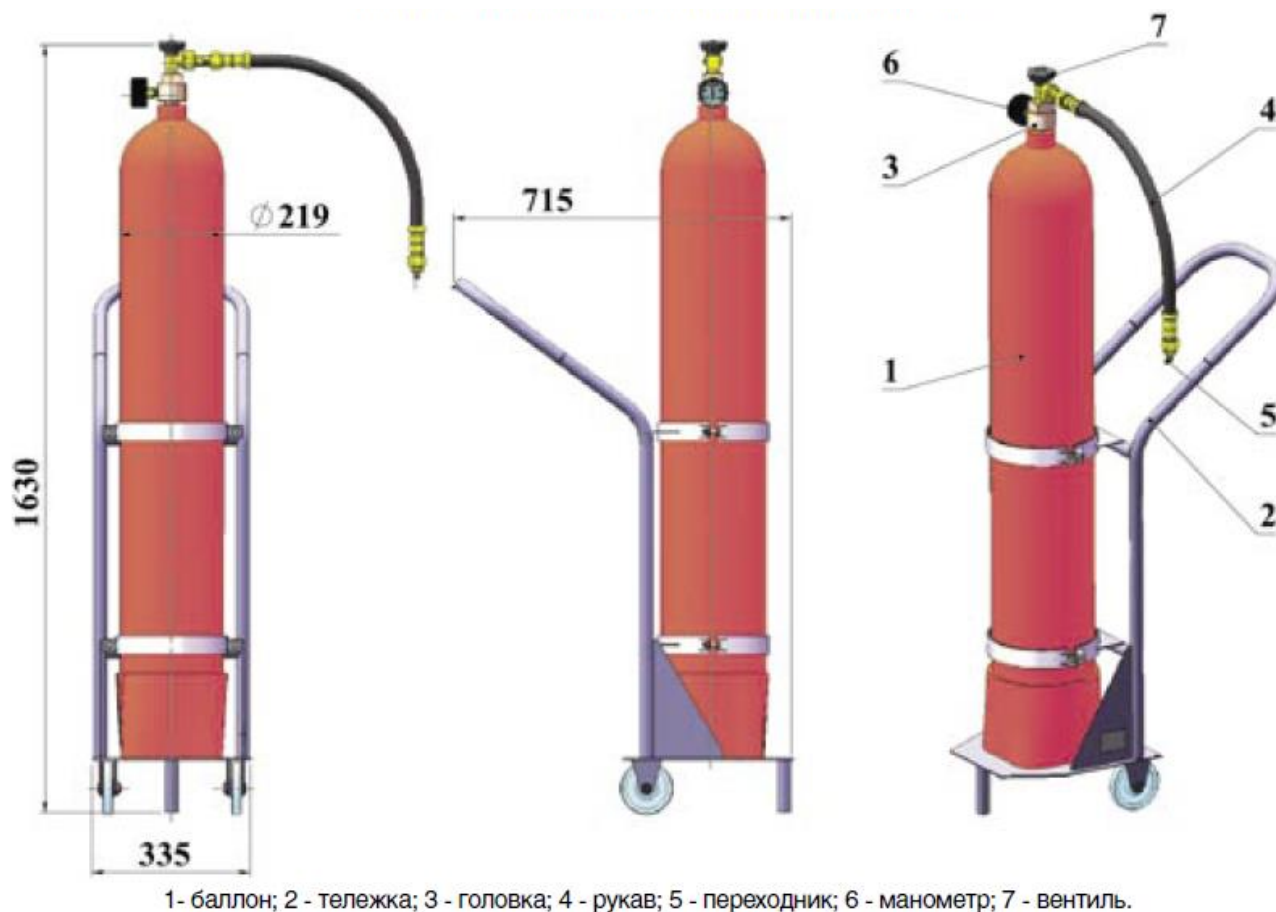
Общий вид и габаритные размеры баллона воздушного передвижного ПЭР-46.02
